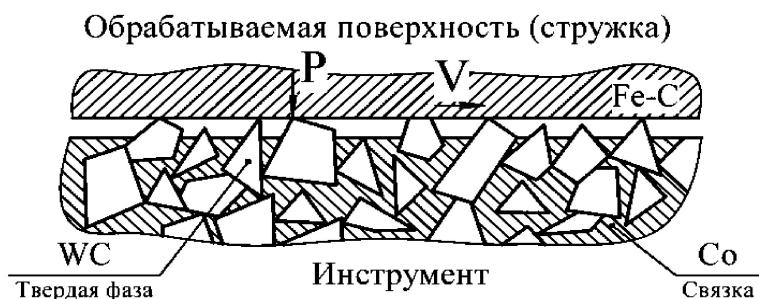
Схема контакта обрабатываемой поверхности и рабочей поверхности твердосплавного инструмента
